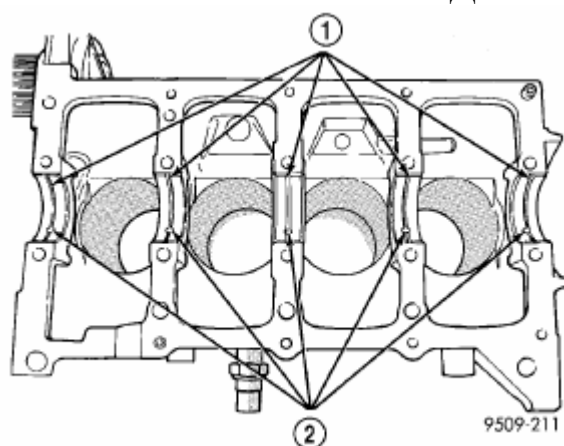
Установка верхнего вкладыша коренного подшипника.
